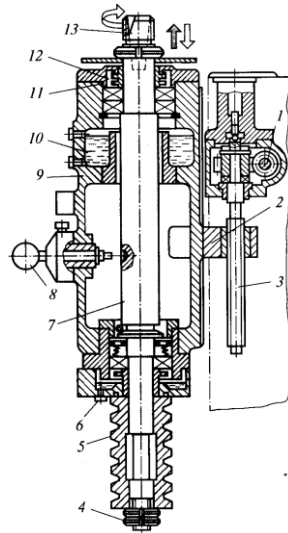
Шпиндельний блок: 1 – черв'як; 2 – кронштейн; 3 – гвинт; 4 – гайка; 5 – шків; 6 – пробка; 7 – шпиндель; 8 – стопор-фіксатор; 9 – корпус; 10 – резервуар для масла; 11 – розприскувач; 12 – гніт; 13 – конусний отвір
